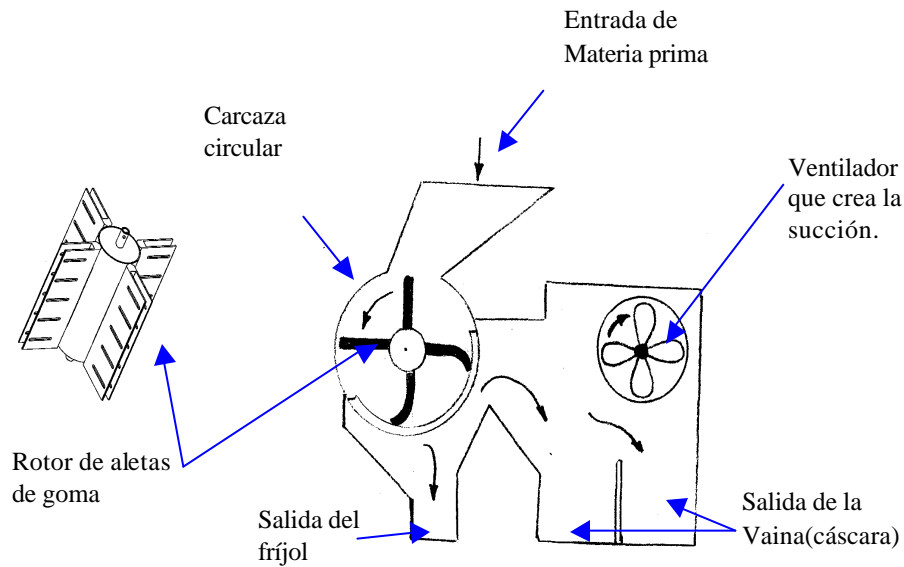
Rotor de Aletas de Goma acoplado a un eje horizontal. Fuente: Héctor Troya
